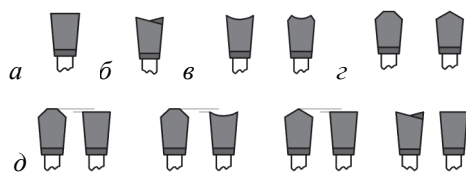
Формы зубьев дисковых твердосплавных пил:
